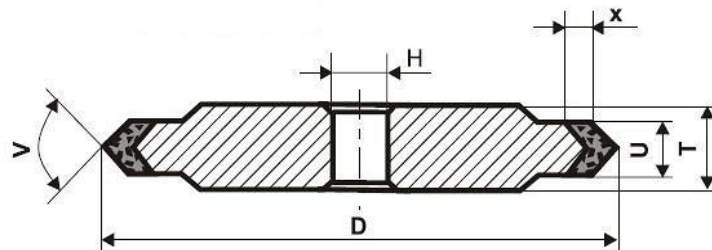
Конусний алмазний круг на металевій зв'язці
